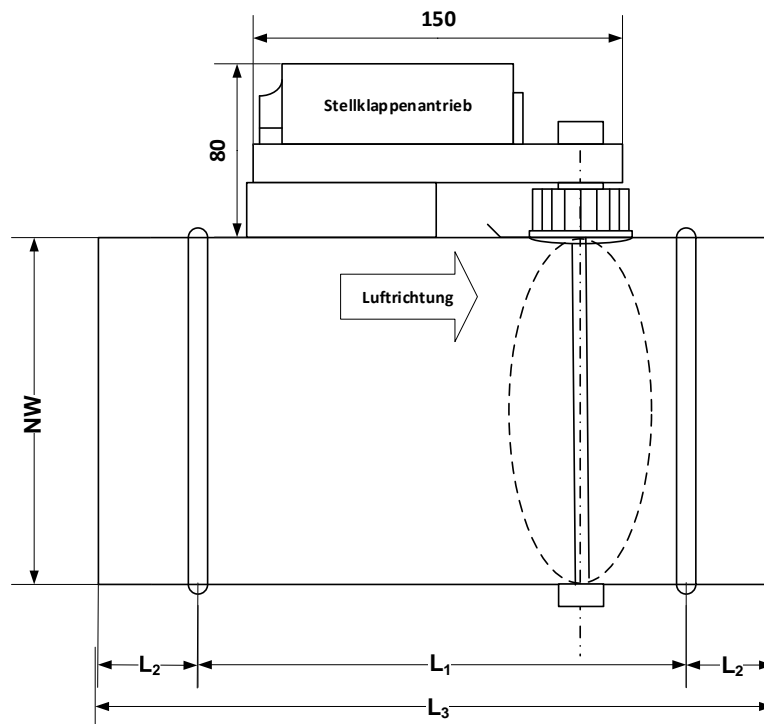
, Abmessungen Stellklappen rund Stahl Rohr/Rohr
